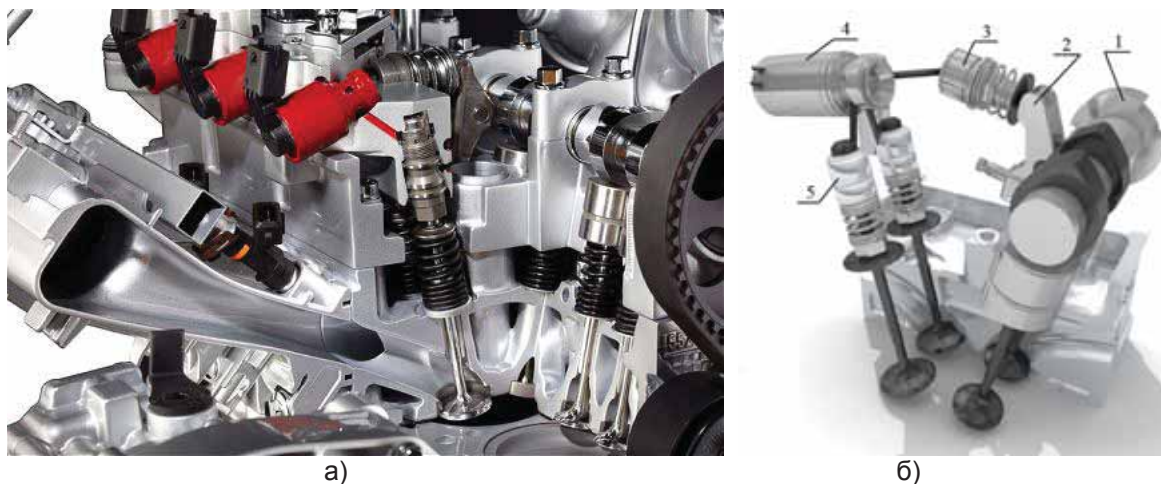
Будова системи Multi Air: а – головка циліндрів двигуна; б – основні агрегати системи Multi Air; 1 – розподільний вал; 2 – коромисло; 3 – головний циліндр; 4 – електромагнітний клапан; 5 – робочий циліндр
